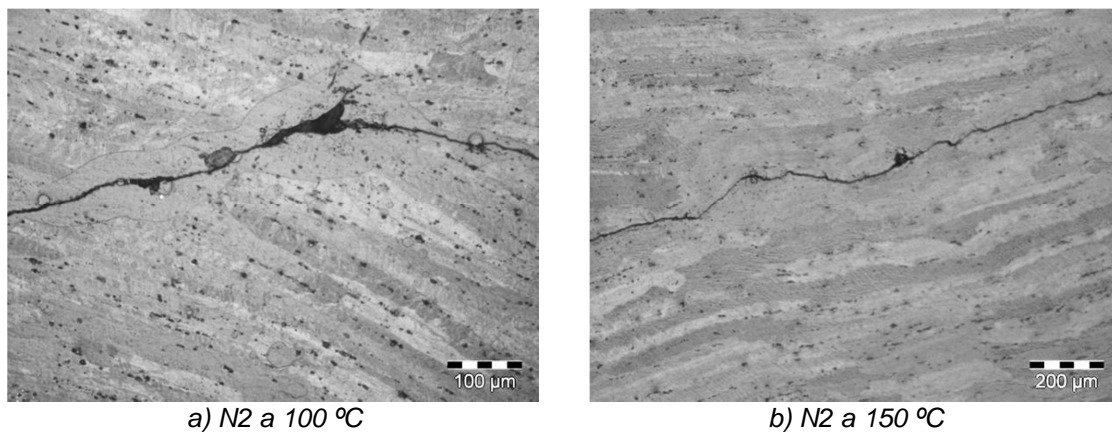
Grietas internas en los álabes forjados.
